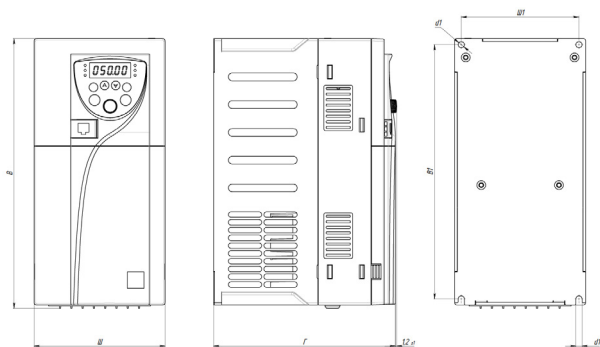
Габаритные и установочные размеры устройств серии INVENT типоразмера 1
